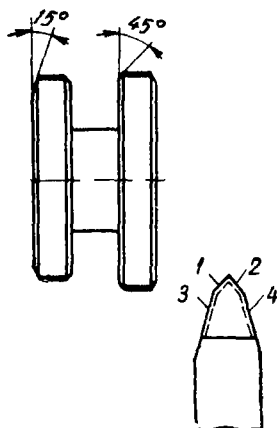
Комбинированный резец для обработки двухвенцовой шестерни
